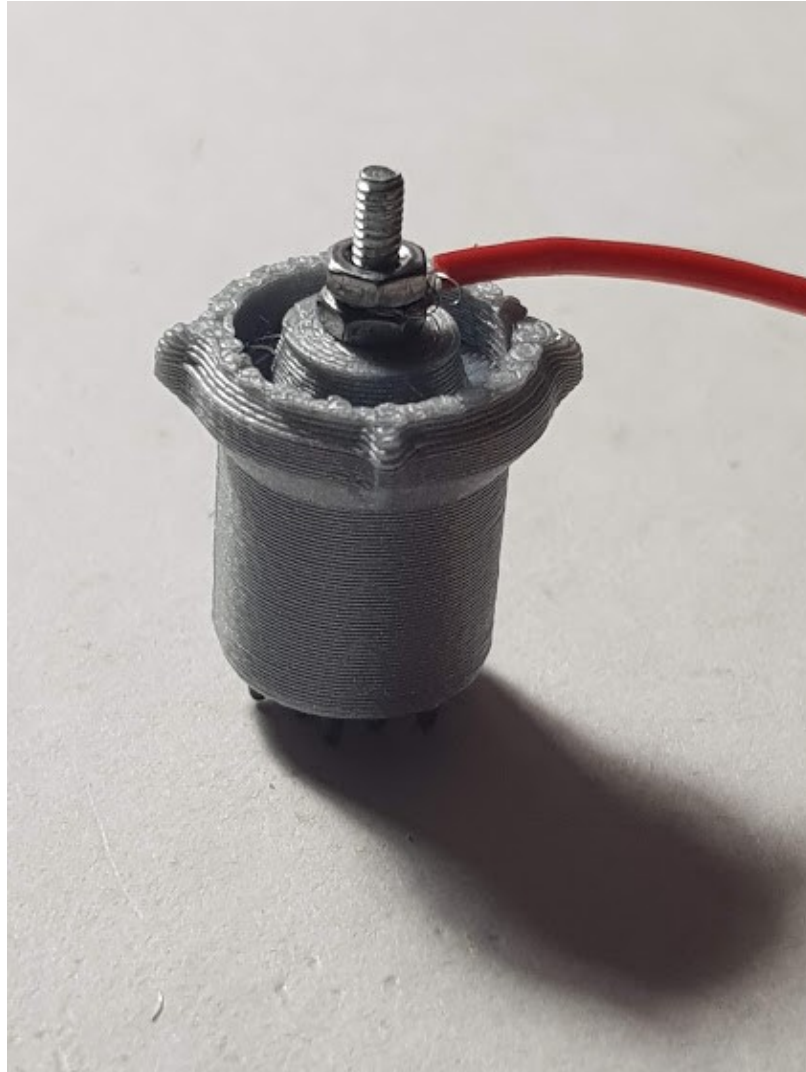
Nodo para electrodos, resorte y tornillo impreso antes de ser ensamblado en el casco.
